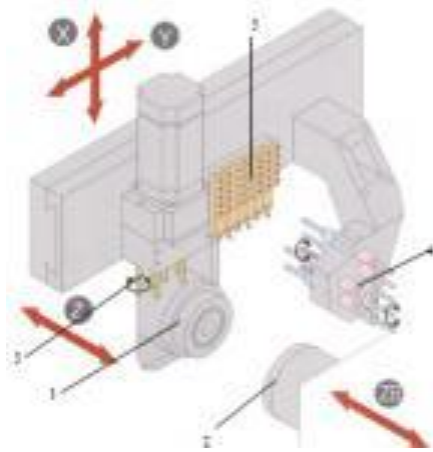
Компоновка станка Diamond 20CS:
